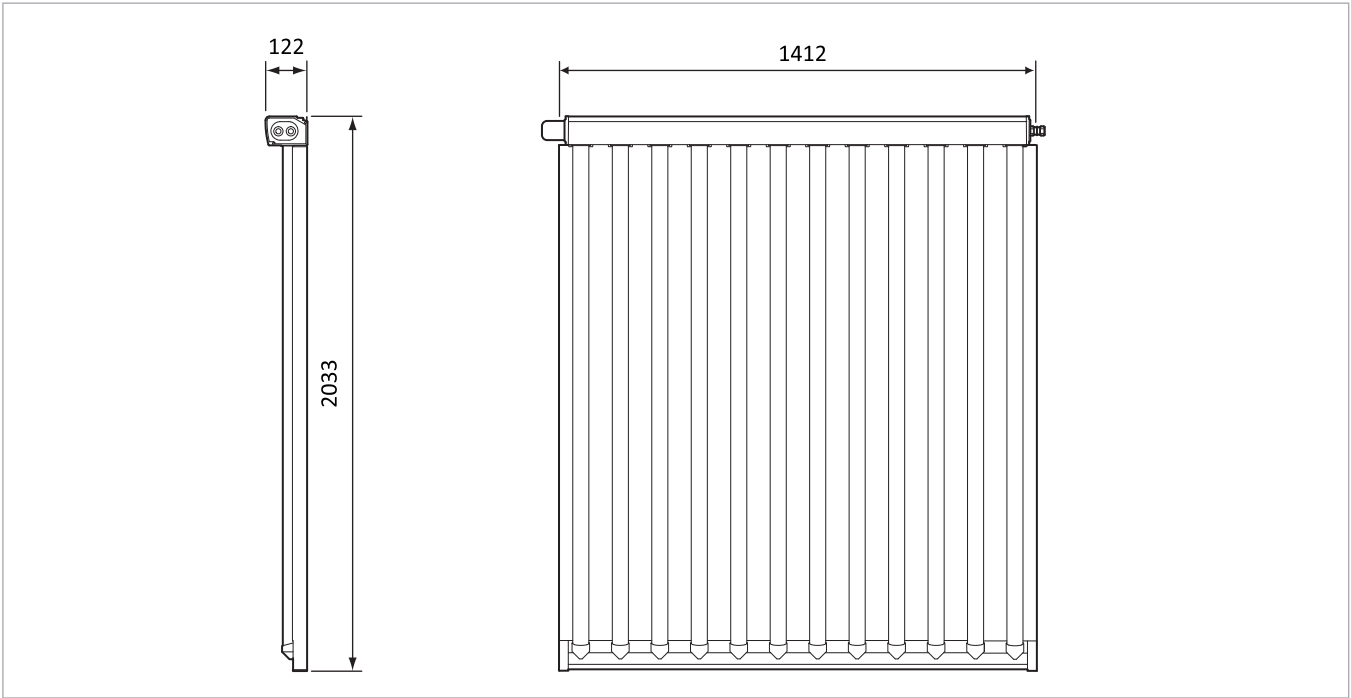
dimensions du capteur à tubes sous vide SolvisLuna LU-304
